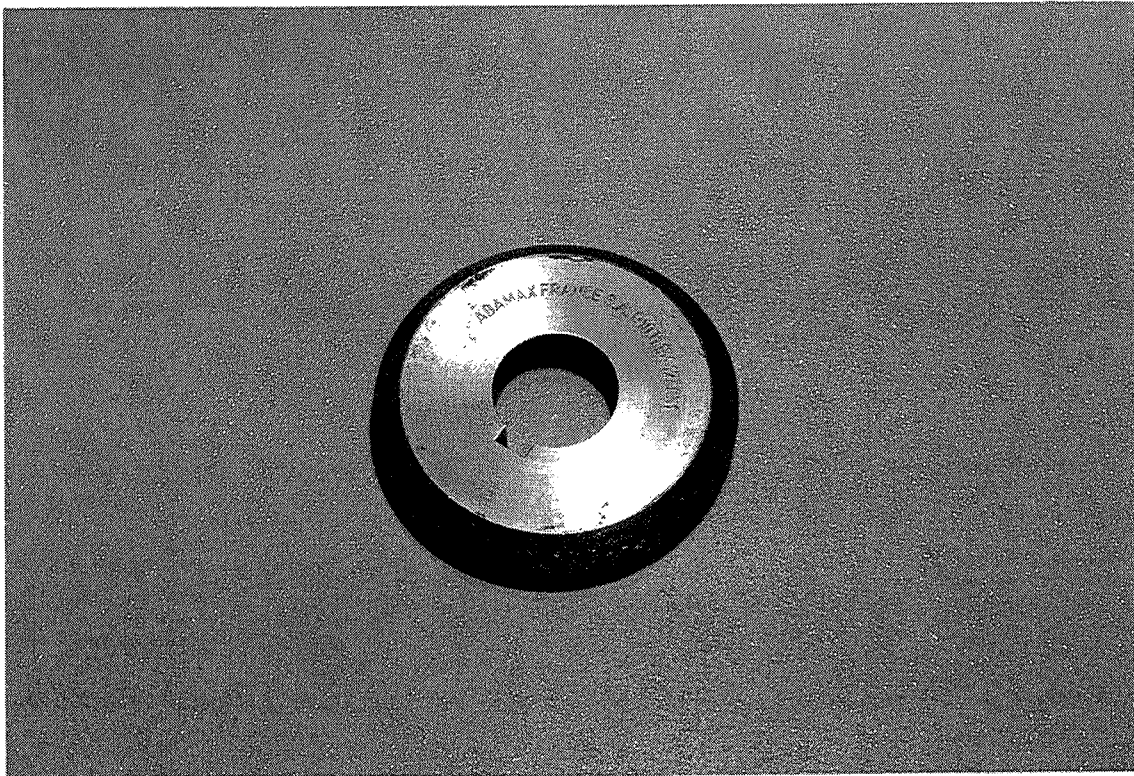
Outil de coupe pour entailler les éprouvettes losipescu.
